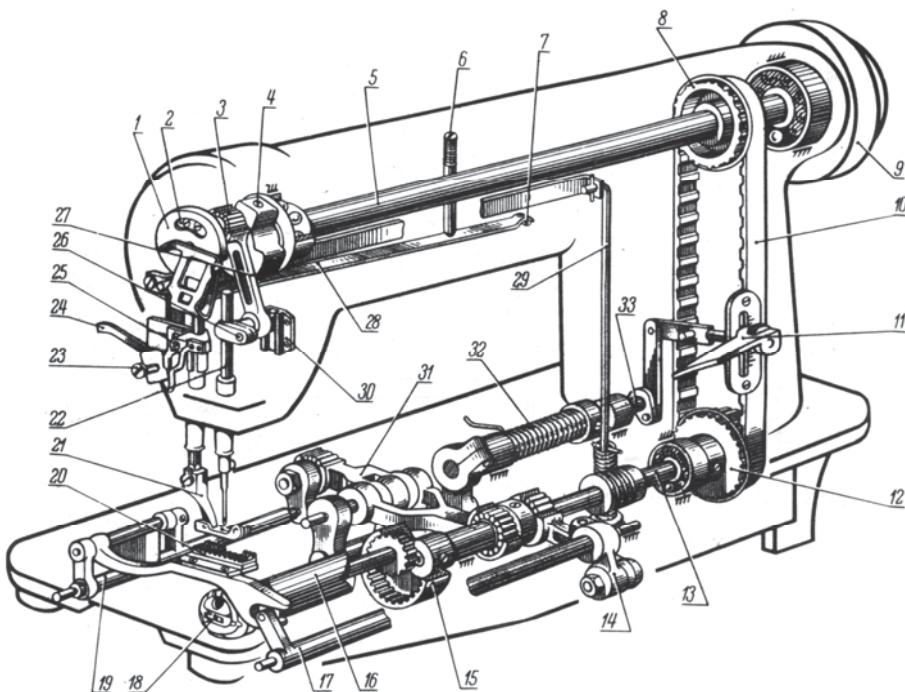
Конструктивно-кінематична схема механізмів швейної машини КУР 97-А:
